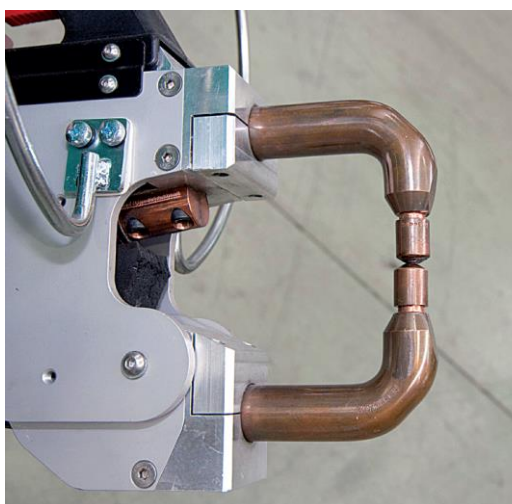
Electrodo de soldadura por puntos. Fuente: CESVIMAP
